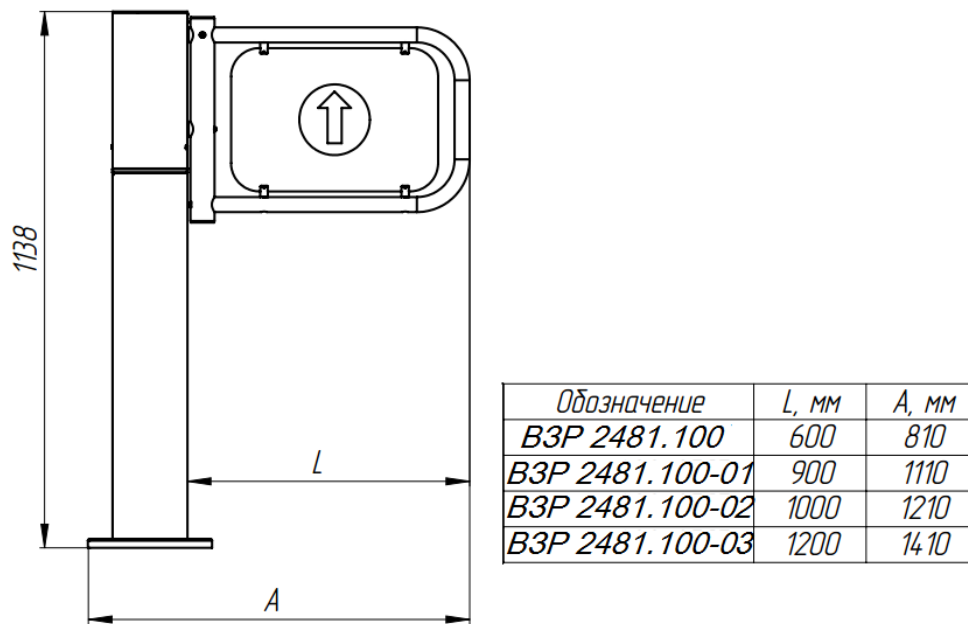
Габаритные размеры изделия для калитки со створкой из металлической трубы.
